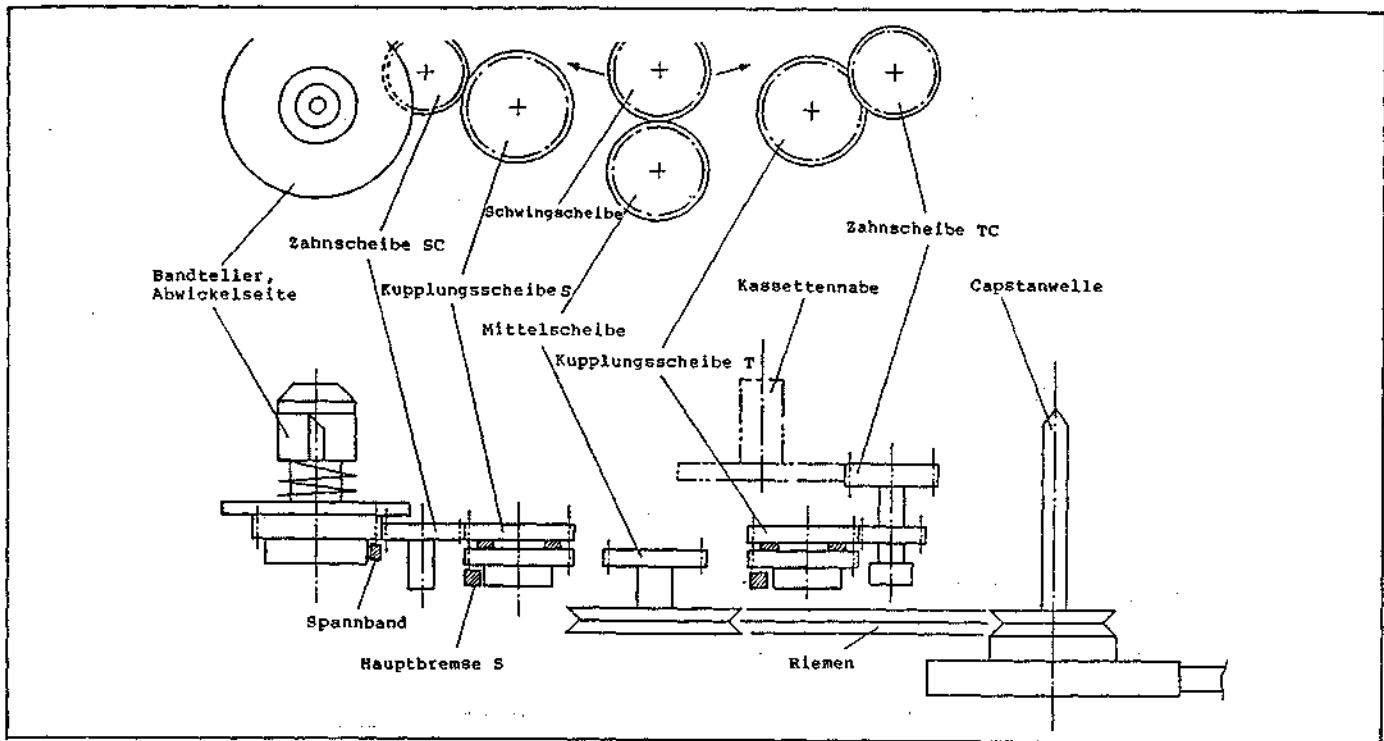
Das Hauptchassis (Seitenansicht)
